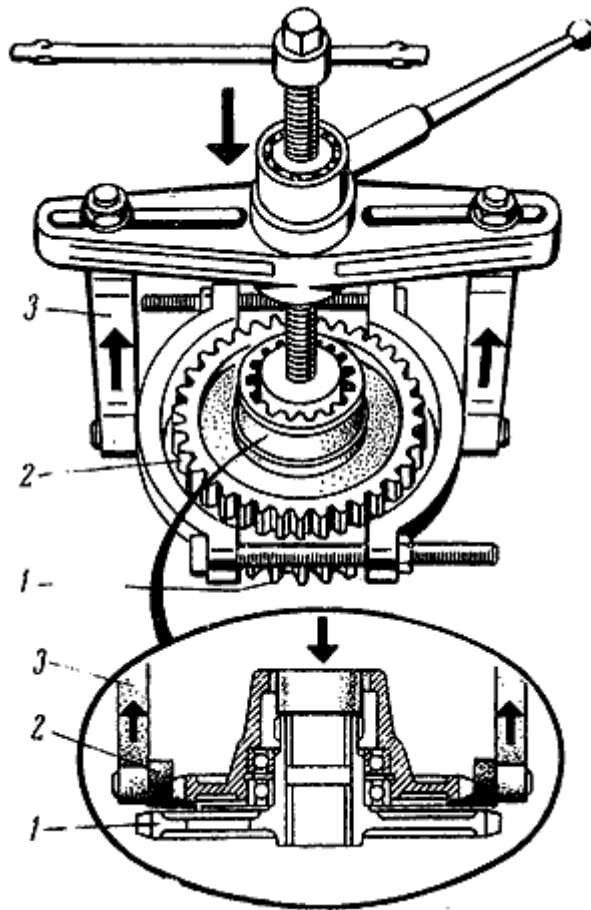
Распрессовка шестерен I и II ступеней привода ВОМ:
